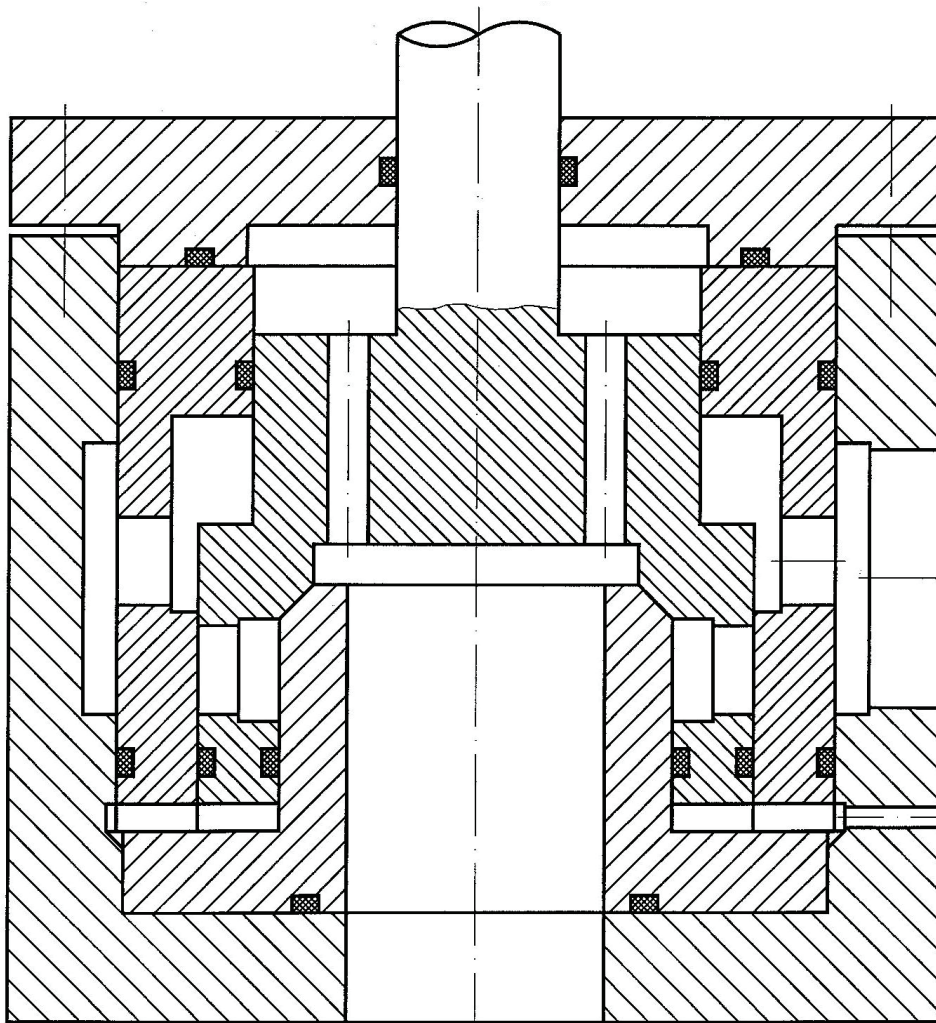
Конструктивная схема запорно-регулирующего клапана с уменьшенным осевым габаритным размером (патент на изобретение RU № 2552211)
